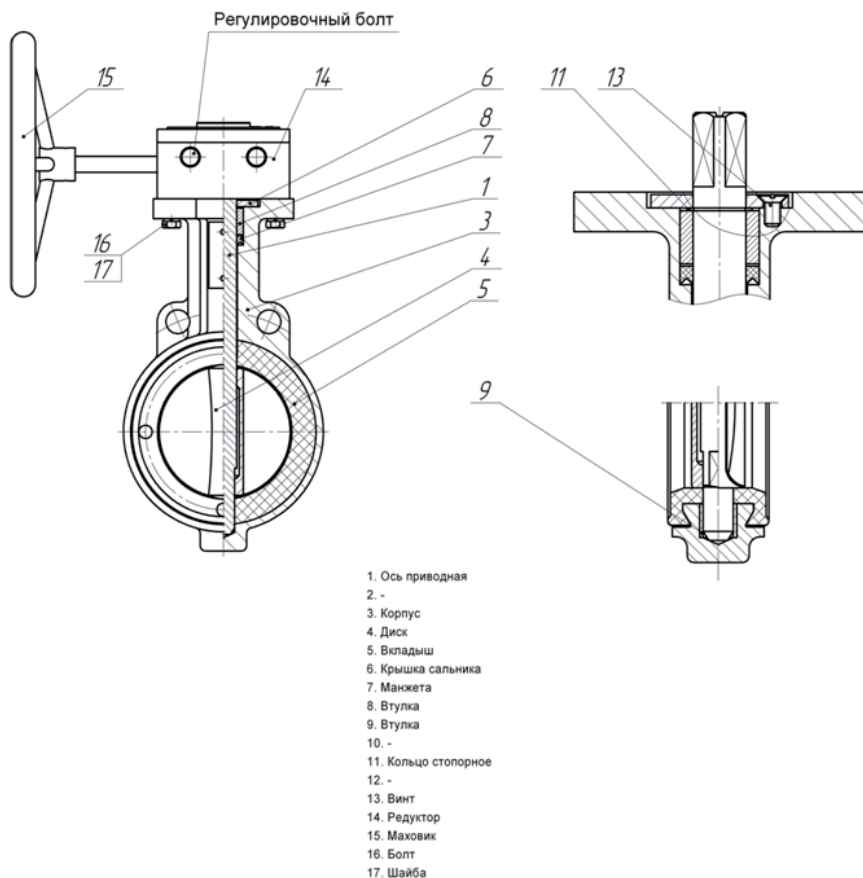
б. Затвор серии «СТАНДАРТ» с редуктором
